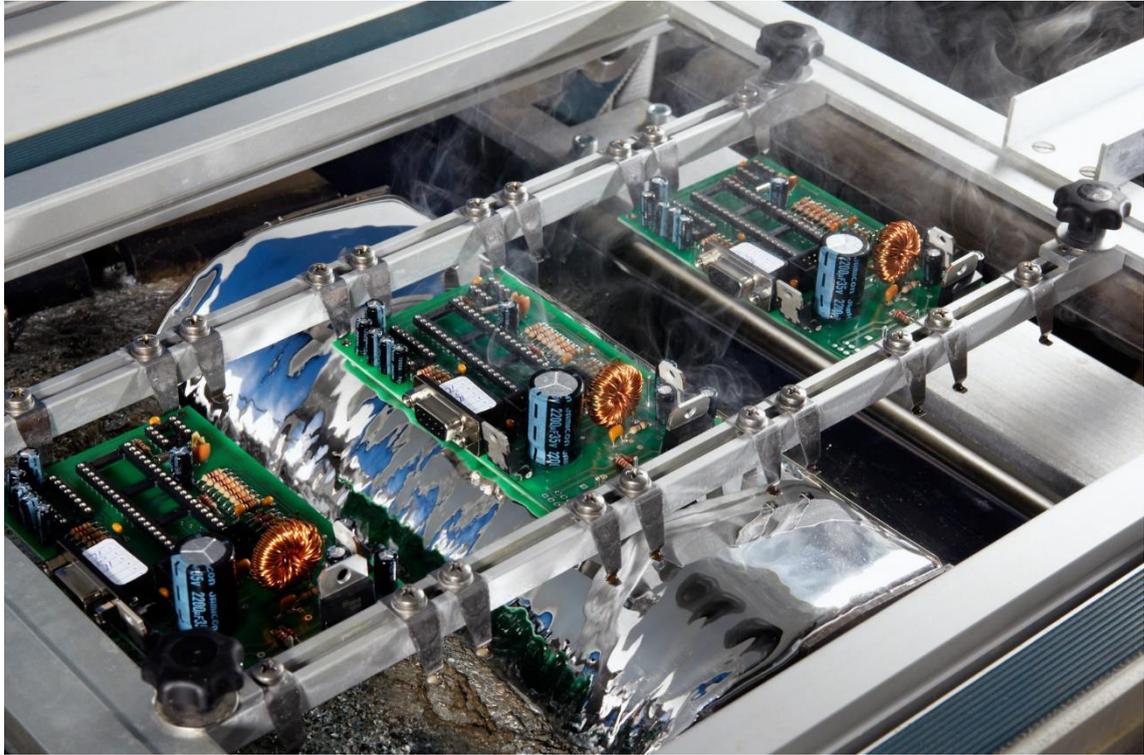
Imagen del funcionamiento de una soldadora por ola (abierta). Nótese como la "ola" de estaño fundido toca la parte inferior de los PCB, soldando los componentes
